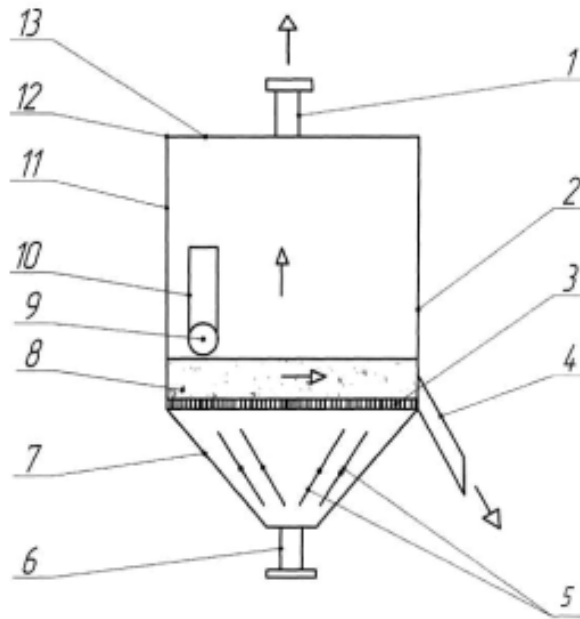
Сушарка: 1,6 – газові патрубки; 2,11 – стінки; 3 – газорозподільний пристрій; 4 – розвантажувальний патрубок; 5 – змонтовані заслінки; 7 – днище; 8 – псевдо-розріджений шар; 9 – газовий канал; 10 – завантажувальний патрубок; 12 – корпус; 13 – кришка
